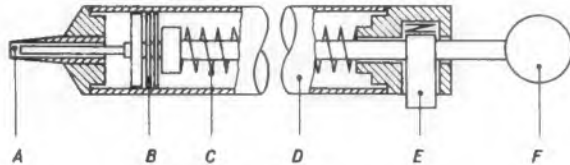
Prinzip des Lötzinn-Schlürfers; A = Ansaugdüse, B = Kolben, C = Spannfeder, D = Zylinder, E = Auslöseknopf, F = Spannknopf
